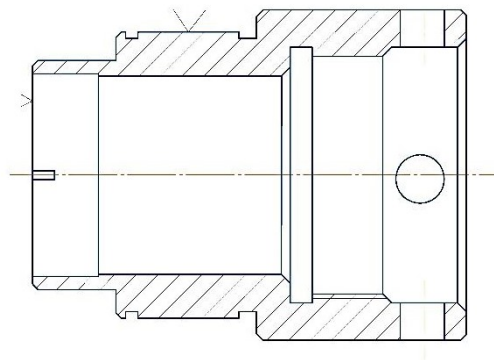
Схема базування заготовки на завершальних операціях
